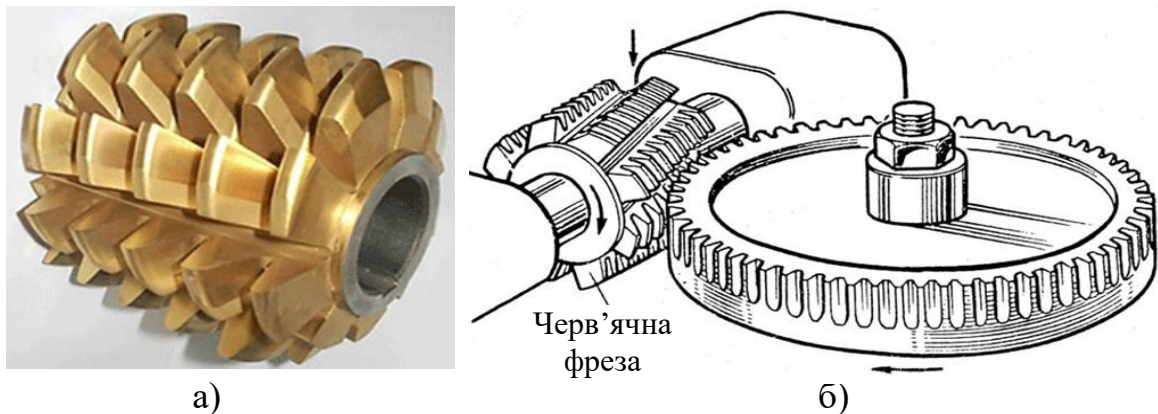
Черв'ячна фреза (а) та схема нарізання шестерні (б)
